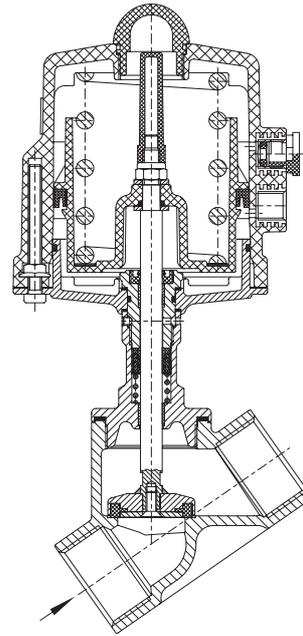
· Válvula de asiento inclinado Tipo 3353
